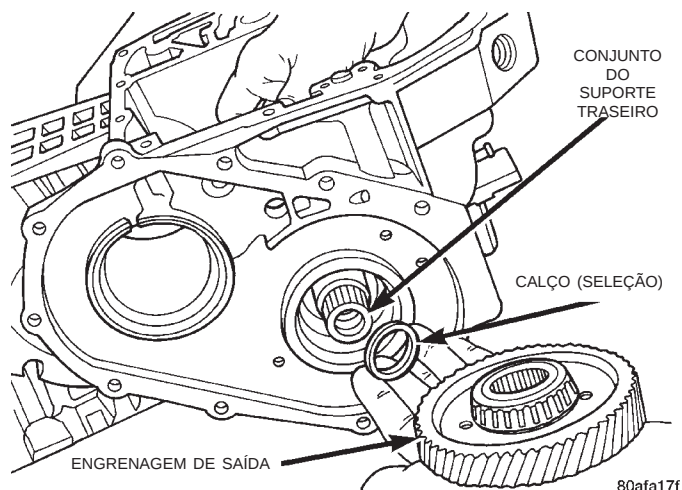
Engrenagem e Calço (Seleção) de Saída
